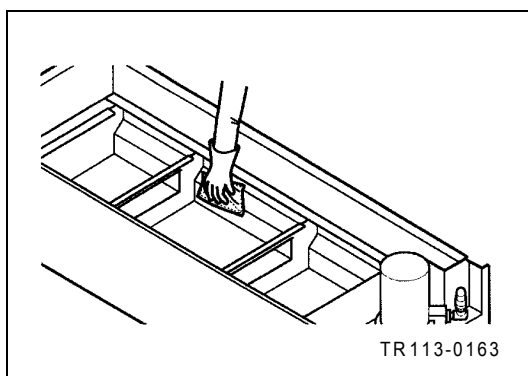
Очистка резервуара СОЖ (2/2)
